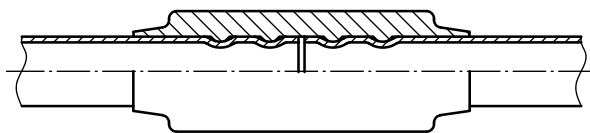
Formgedächtnis-Verbinder, dauerhaft
